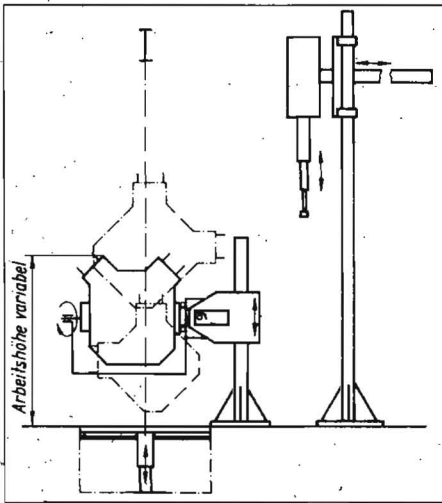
Prinzipskizze einer Demontageeinheit für Motoren mit programmgesteuertem Schrauber
